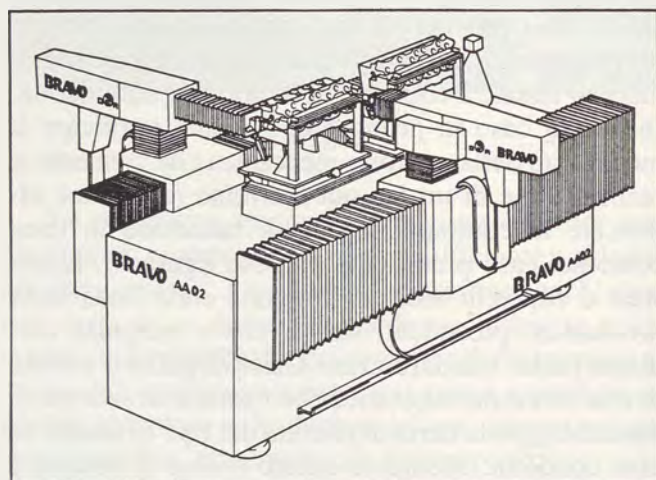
Robot di misura BRAVO AA02, 2 bracci: Collaudo di una testa cilindri (getto in lega di alluminio).
